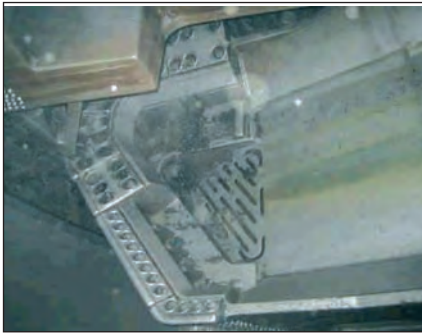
Grilles d'égouttage le long du canal à déblais.
